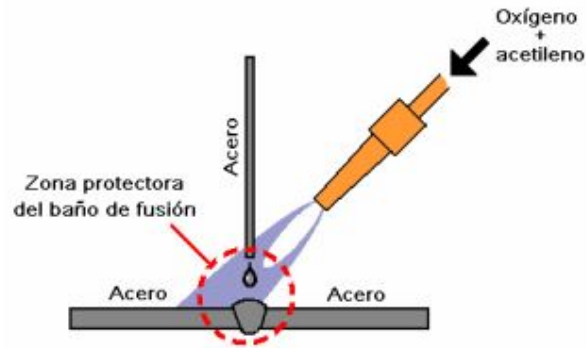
Soldadura oxiacetilénica. [24]
